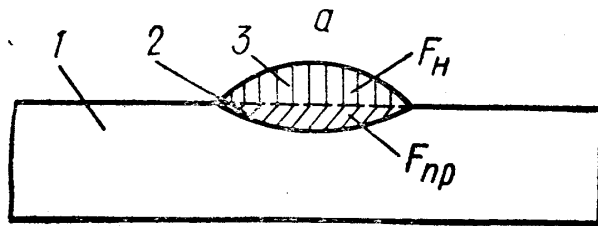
Поперечний переріз валика: 1 — основний метал;
